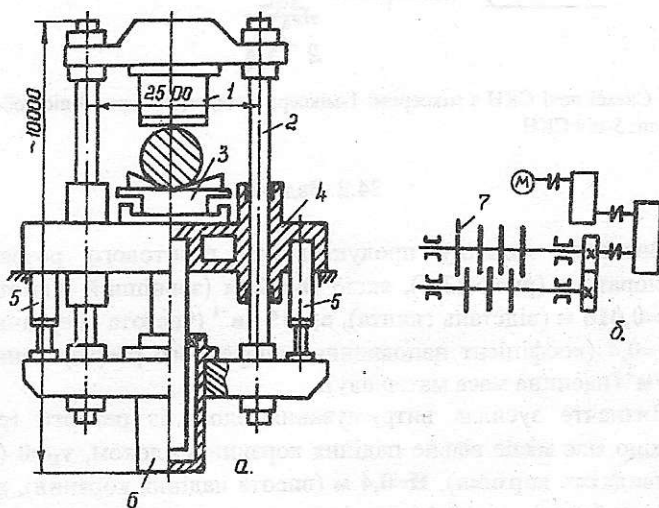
Схеми устаткування для роздрібнювання титанової губки: а-гідропрес для крупного роздрібнювання; б-дискова (чи клинова) дробарка для середнього і дрібного роздрібнювання; 1-ніж; 2-колони; 3-рухомий стіл; 4-нерухома траверса; 5-допоміжні гідроциліндри; 6-головний гідроциліндр; 7-вал з дисками (чи клиноподібними ножами)
